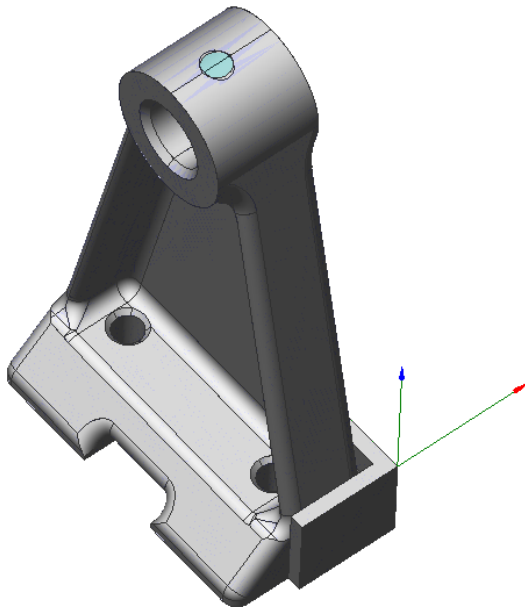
Базування та нульова точка координат заготовки при Базуванні 4
